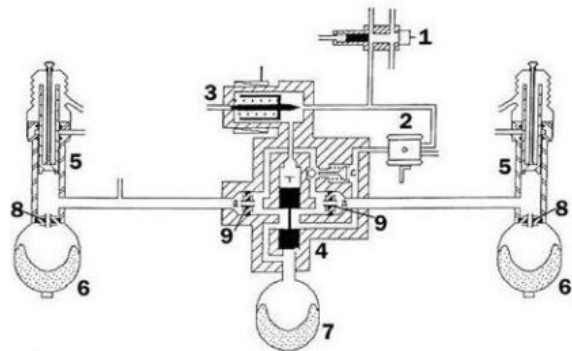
Схема работы гидропневматической подвески: 1 - предохранительный клапан-распределитель; 2 - регулятор положения кузова; 3 - электромагнитный клапан; 4 - регулятор жесткости; 5 - гидравлический цилиндр; 6 - основной гидропневматический упругий элемент; 7 - дополнительный гидропневматический упругий элемент; 8 - основной амортизаторный клапан; 9 - дополнительный амортизаторный клапан.
